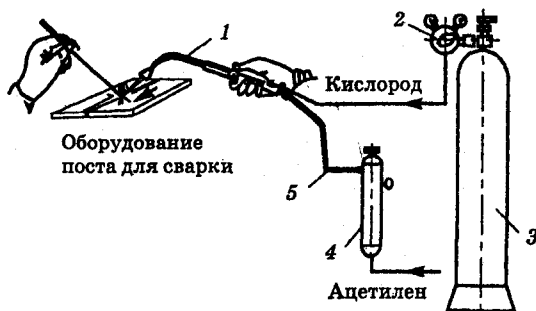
Оборудование поста для газовой сварки:
